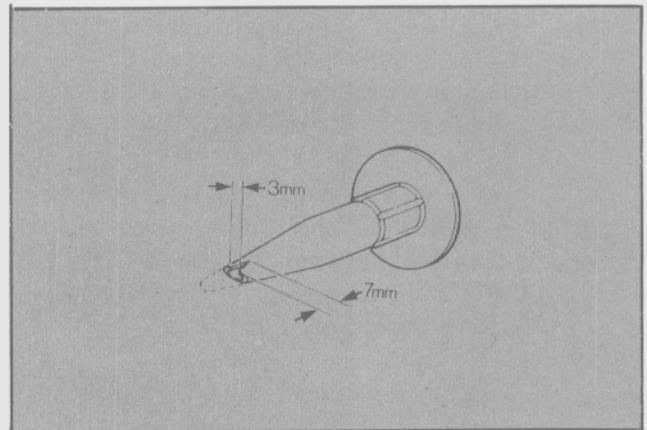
Segundo corte a realizar en la boquilla aplicadora de adhesivo.
